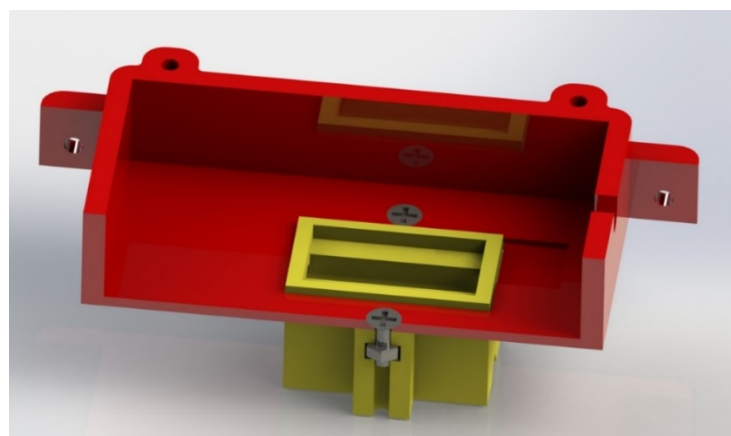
Vista em corte da montagem entre o suporte e a caixa
